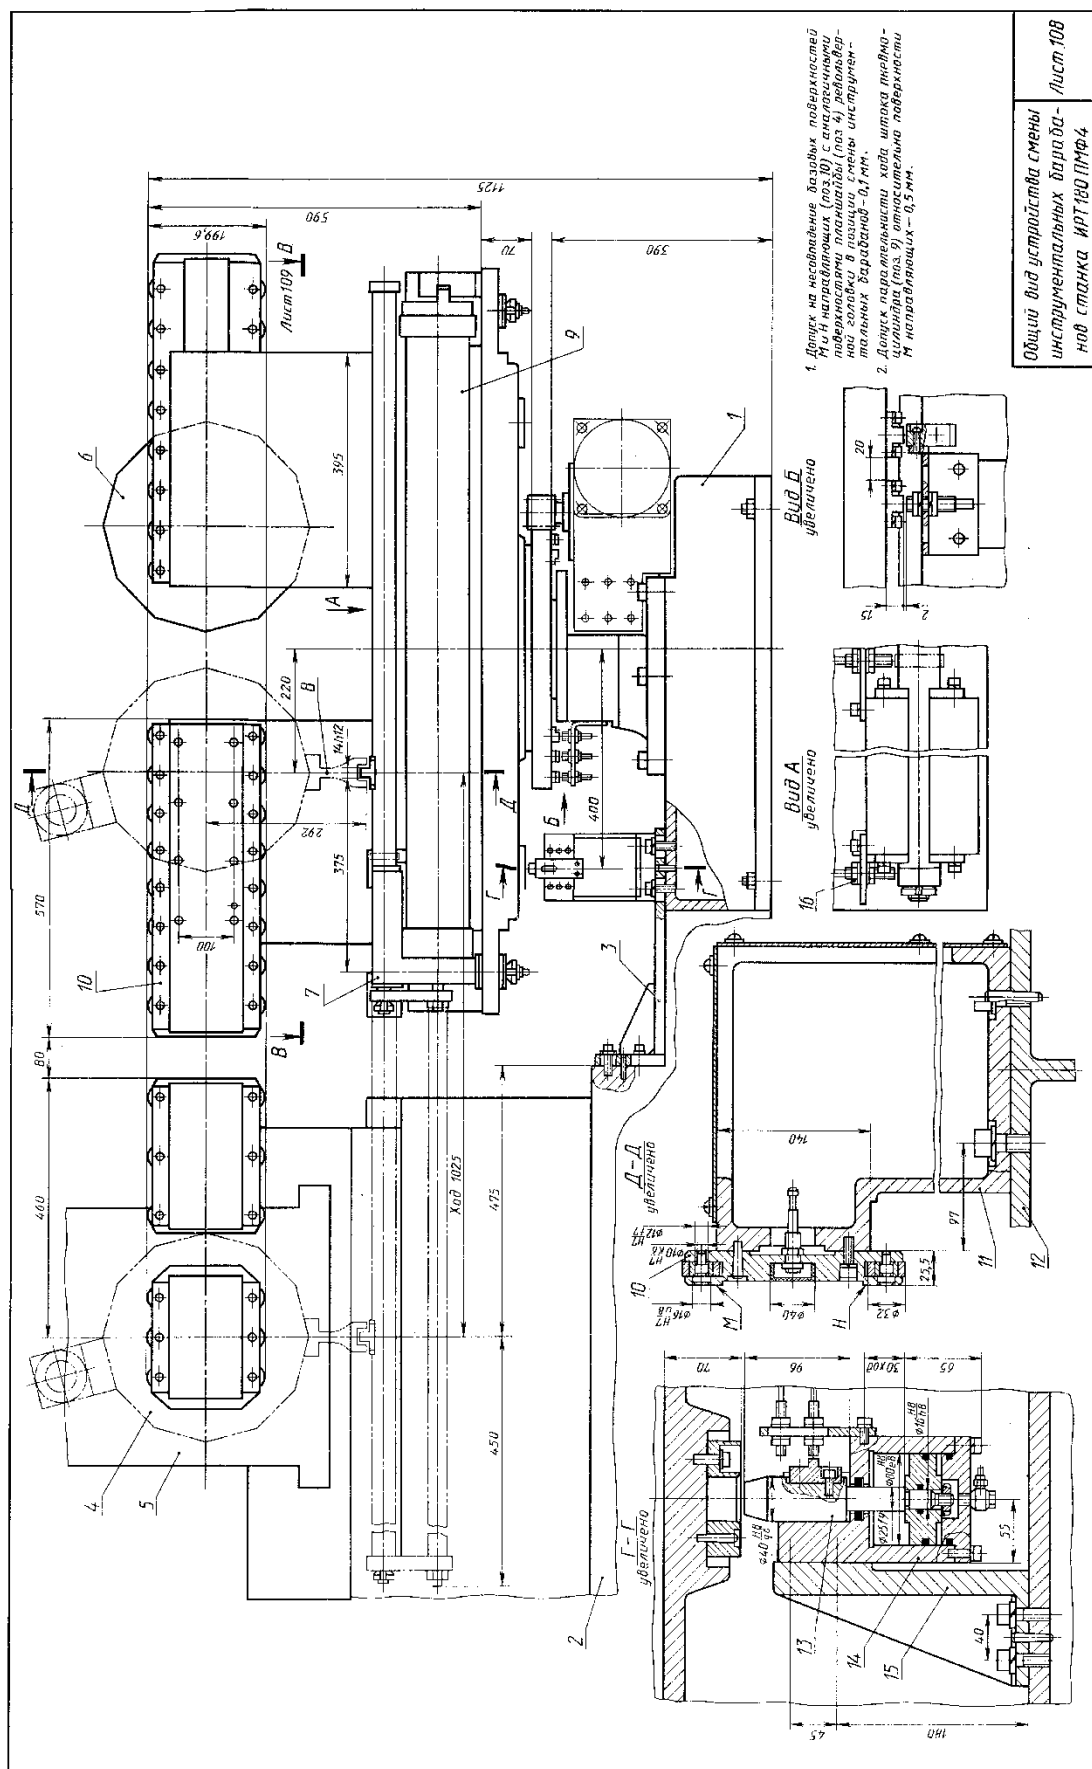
Загальний вид пристрою зміни інструментальних барабанів верстата ІРТ180ПМФ4
